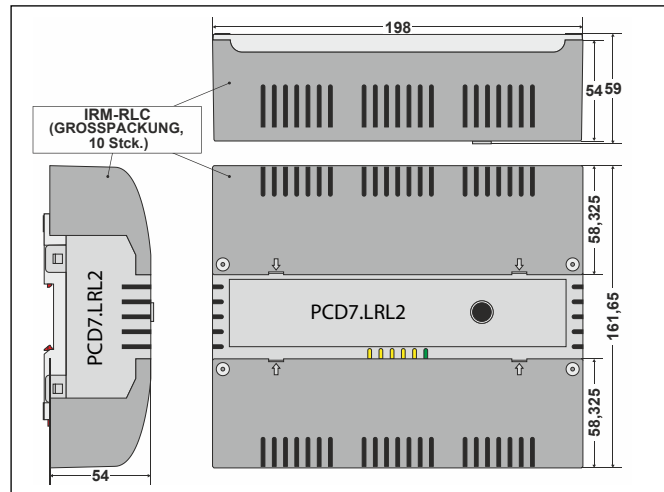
Grand boîtier, avec caches de protection des bornes, dimensions (en mm)
